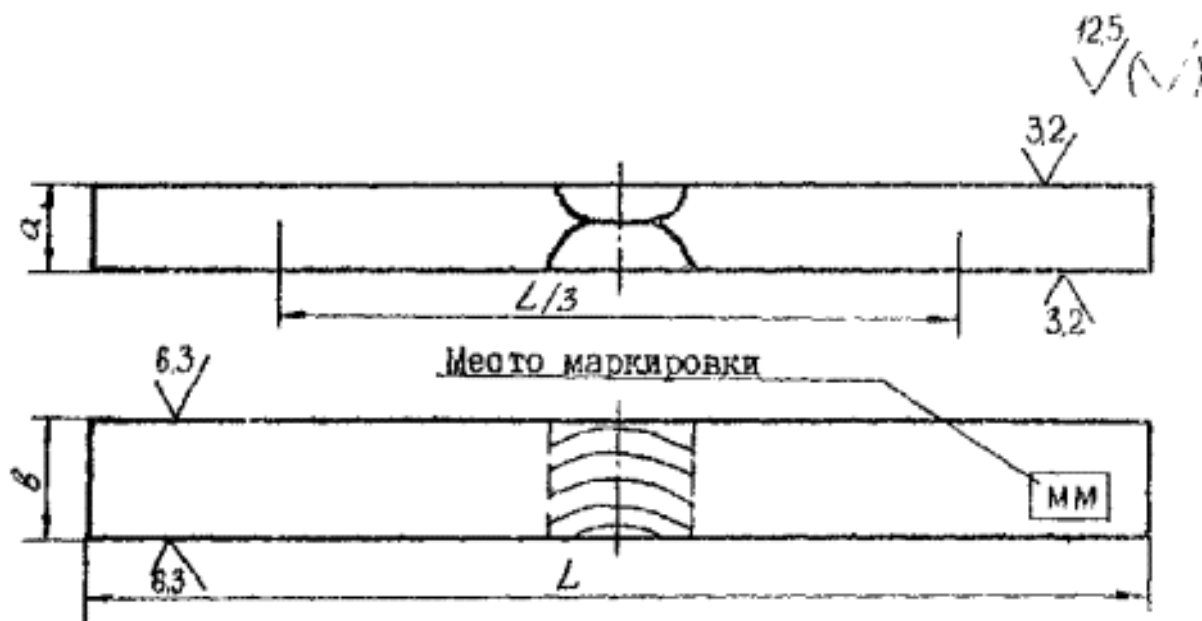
Образец на статический изгиб сварного соединения толщиной основного металла до 60 мм
